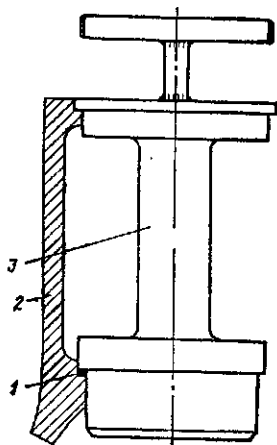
Приспособление для калибрования эпоксидной композиции в блоке цилиндров.
